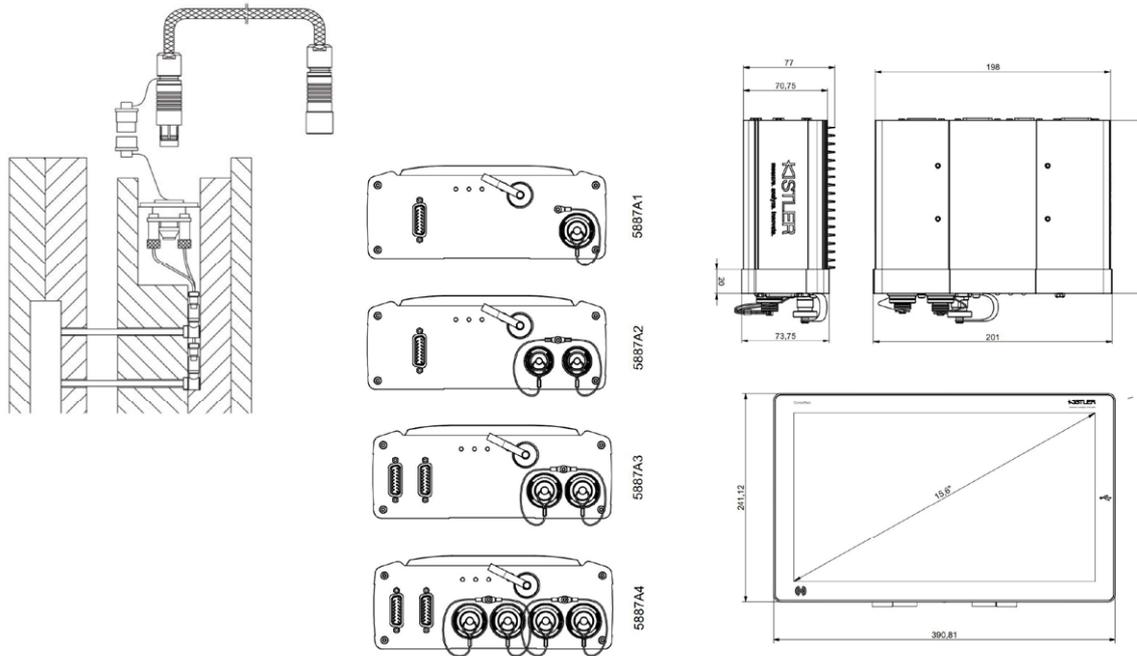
Kraftsensor für die indirekte Werkzeuginnendruckmessung hinter einem Auswerferstift im Spritzgießwerkzeug
